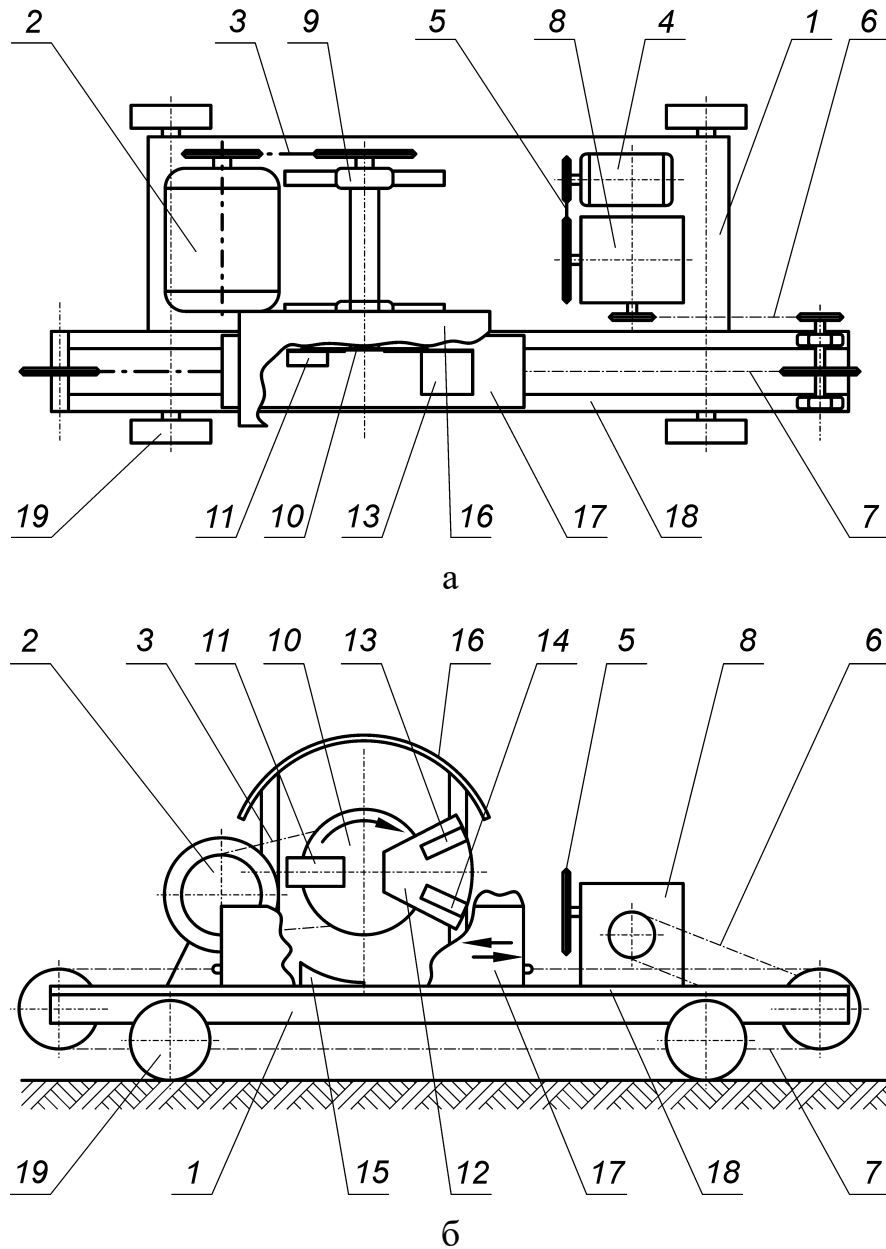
Схема лабораторной установки: а — вид сверху; б — вид сбоку
